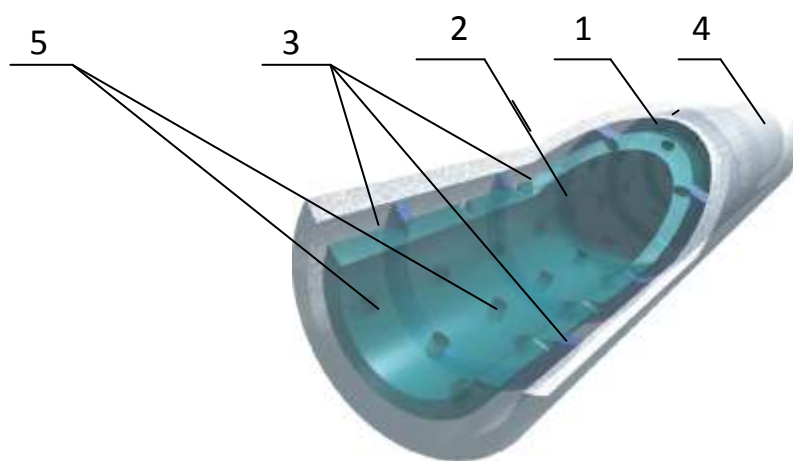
Конструкция каркасного трубчатого полипропиленового аэратора
